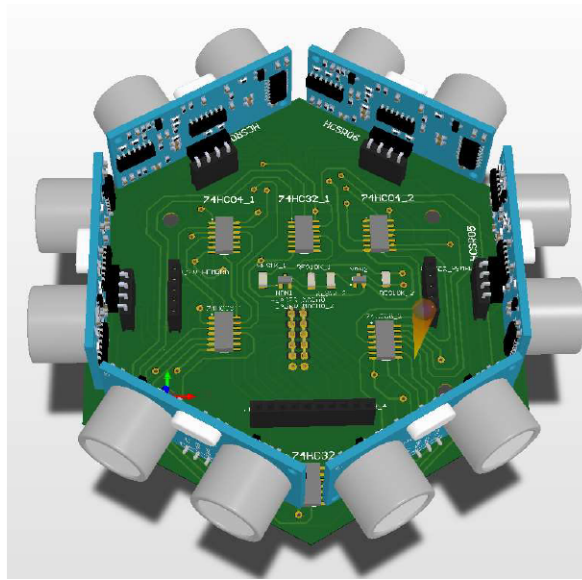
Diseño CAD de falda de 6 sensores ultrasónicos junto con placa PCB de control de estos sensores [1].
